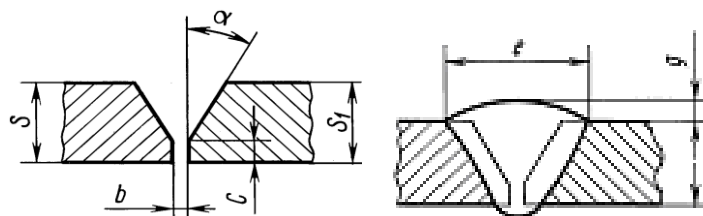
Форма разделки кромок и сварного шва С-17 по ГОСТ 16037-80
